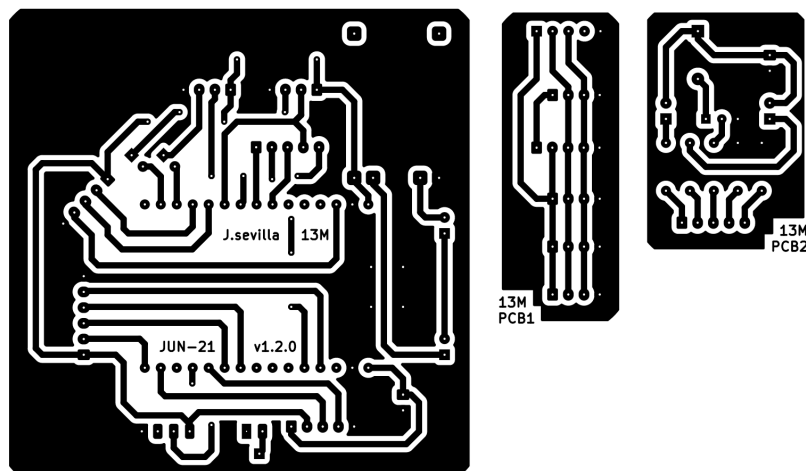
Diseño final de la placa impresa en 3 secciones.
